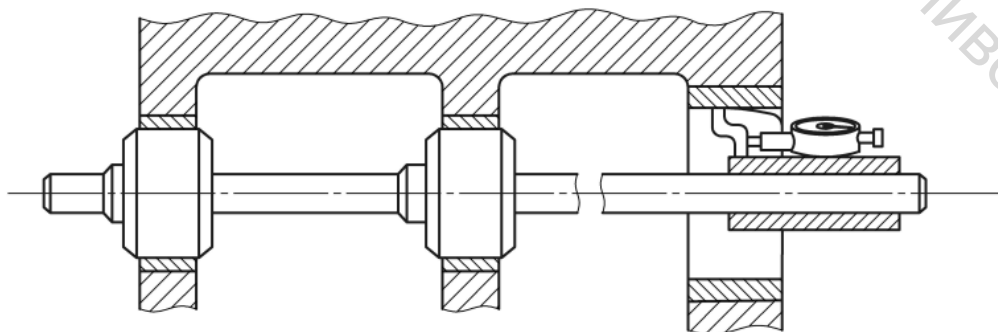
Схема проверки соосности подшипников в сборочных единицах повышенной точности
